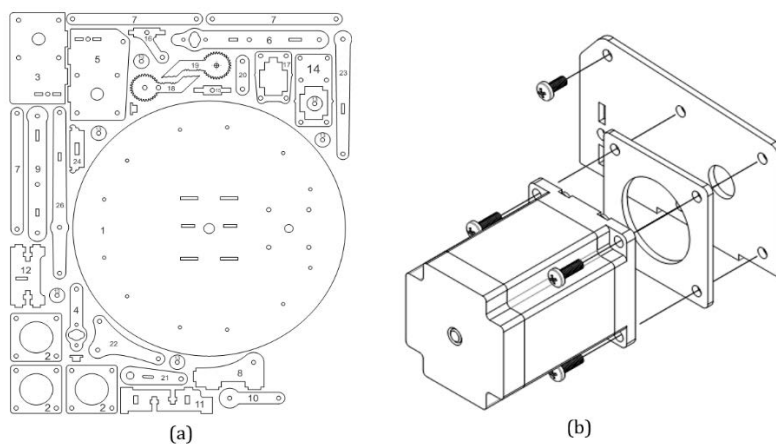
(a) planos para corte Láser de las piezas del brazo. (b) Ejemplo de esquemas de ensamble de secciones
